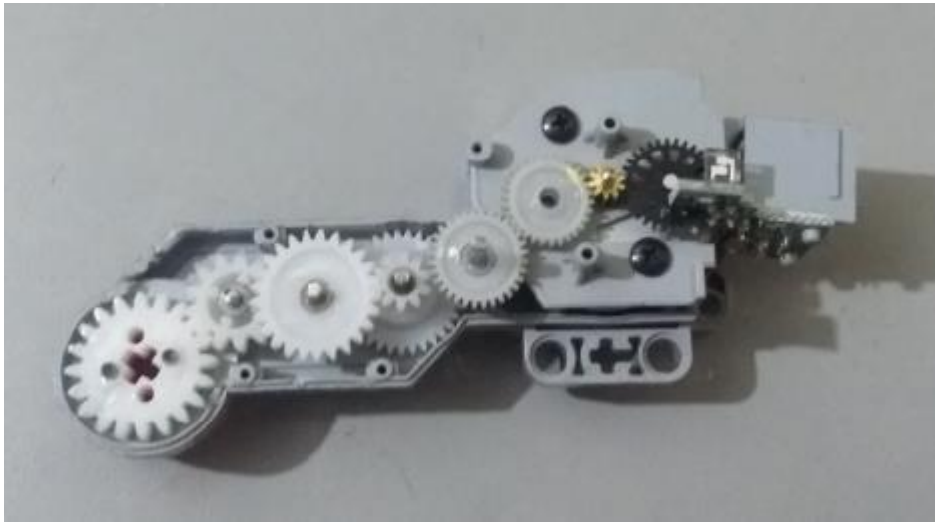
Diseño interno de Motor Grande EV3. Fuente: (Propia).
